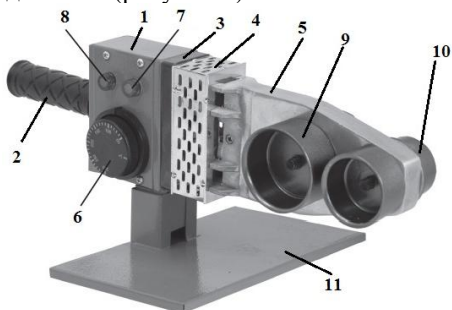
Сварочный аппарат СВА-900
